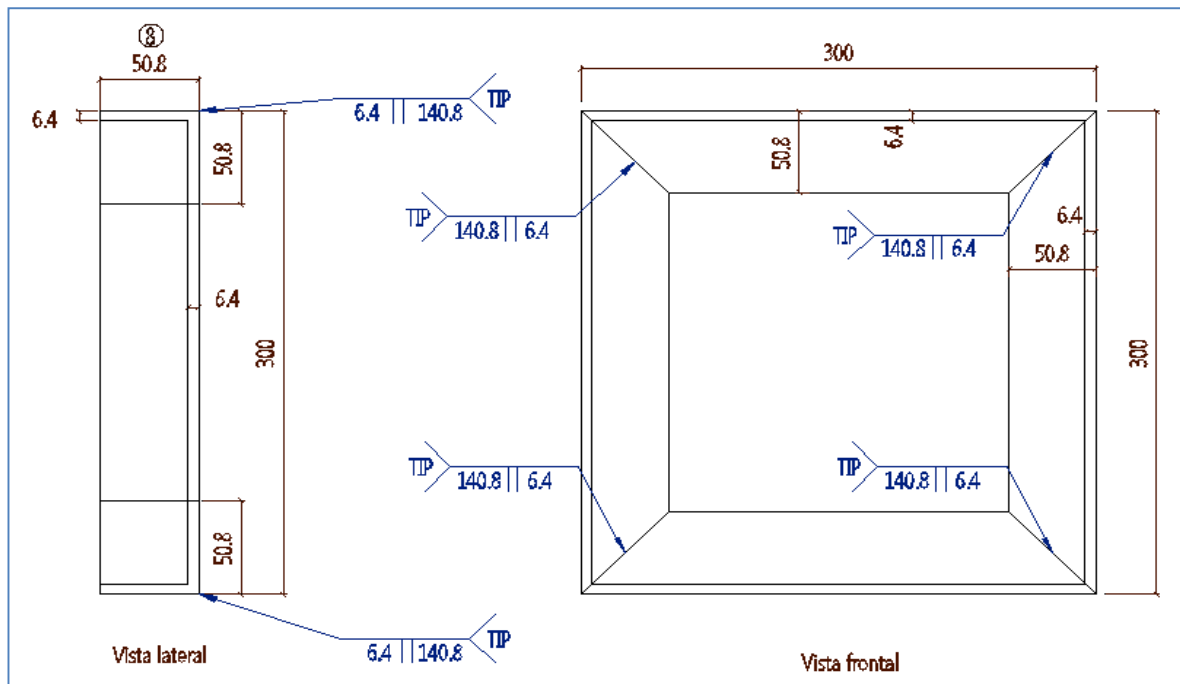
Detalle despiece pieza No.8 modelo 4 tensión.
